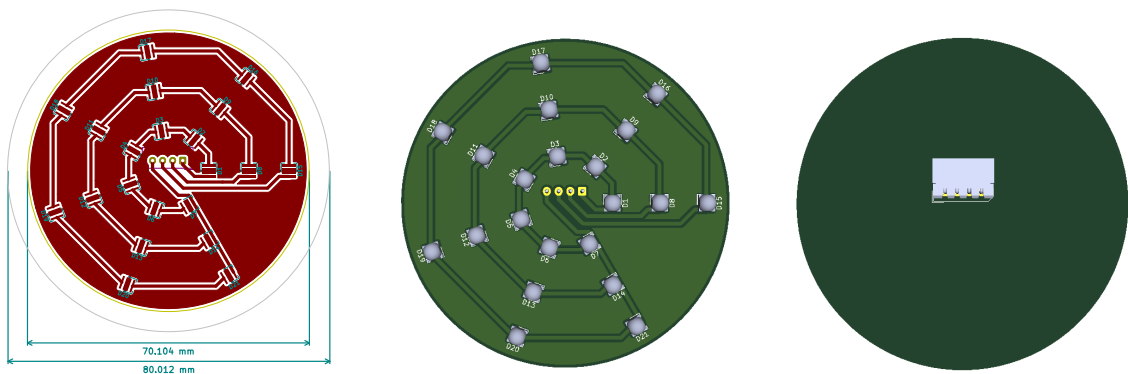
Dimensão e visão superior e inferior da PCB do sistema de iluminação.
